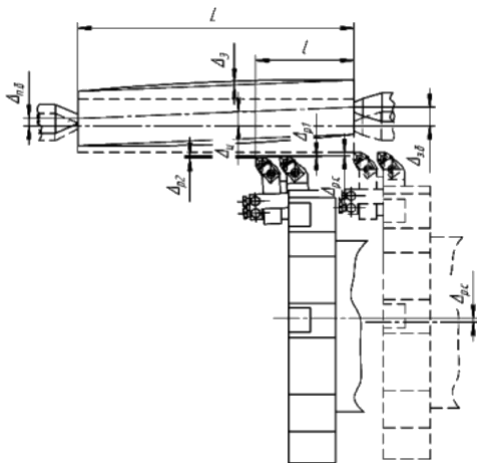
Схема формування похибки обробки при використанні комбінованого різця
